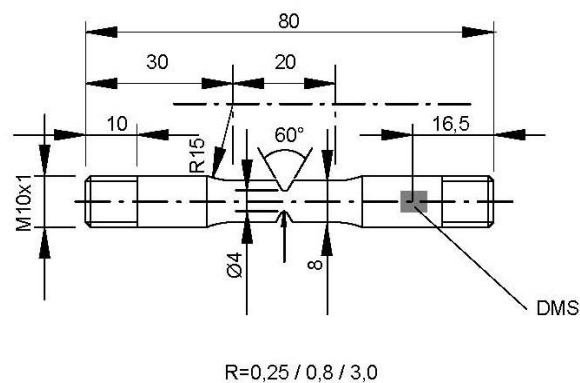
Geometrie und Hauptabmessungen der Kerbzugproben
